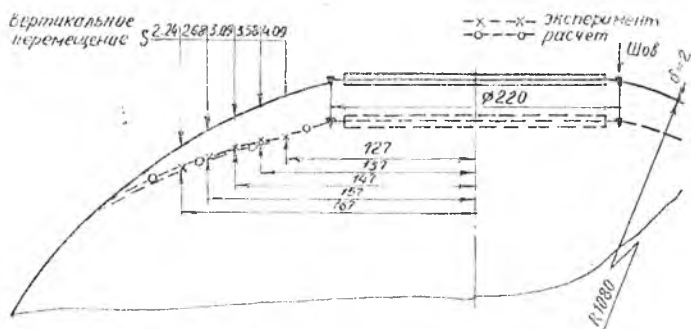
Прогиб оболочки при сварке фланца из АМгб
